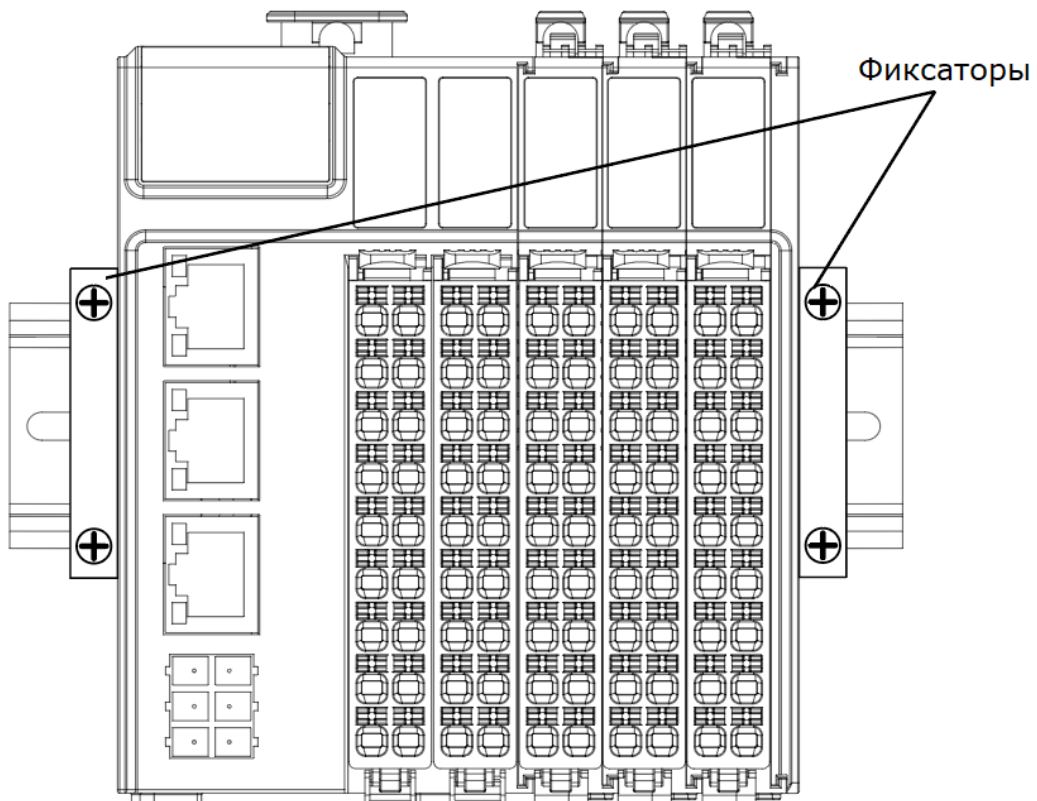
Второй шаг установки сборки устройств на DIN-рейку
